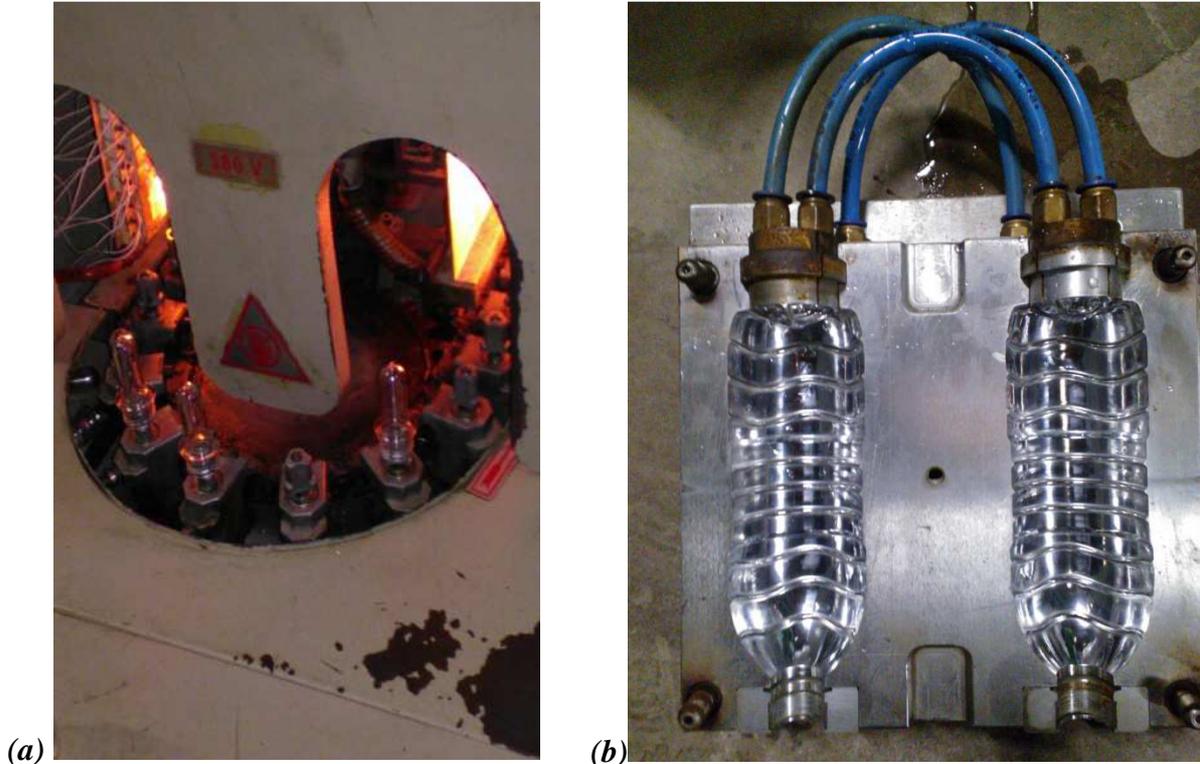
(a) système de préchauffe des préformes (b) moule bouteille PET 1 l orinaire
